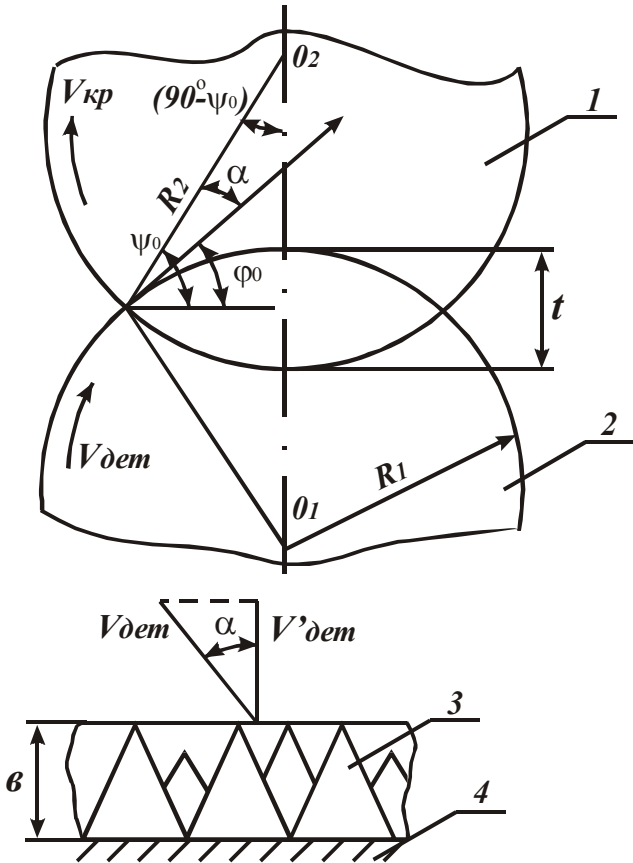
Расчетная схема круглого продольного шлифования: 1 – круг; 2 – деталь; 3 – зерна круга; 4 – связка круга.
